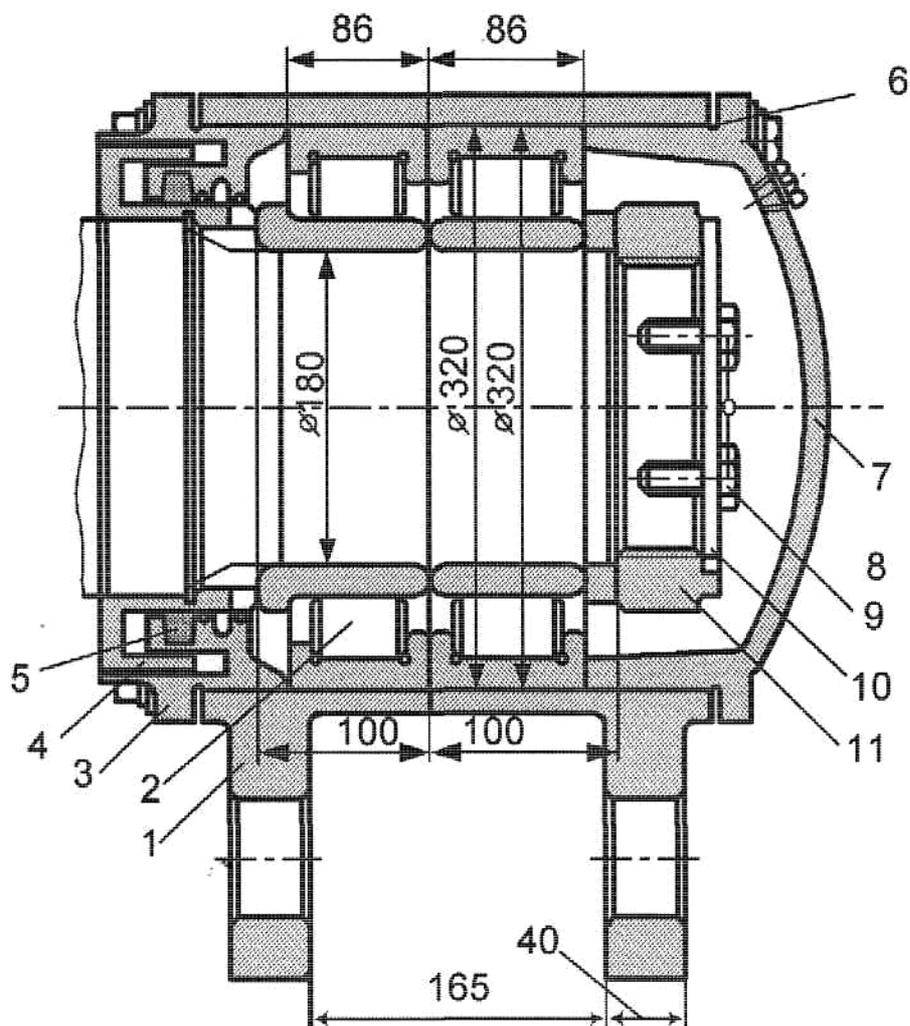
Букса электровоза ВЛ80: 1 - кронштейн с отверстиями для крепления нижней рессоры; 2 - роликовые подшипники; 3 - заднее (внутреннее) кольцо; 4 - лабиринтное кольцо; 5 - сальник; 6 - прокладка; 7 - передняя крышка; 8 - проволоочная обвязка; 9 - болты; 10 - замочная пластина; 11 - гайка;
